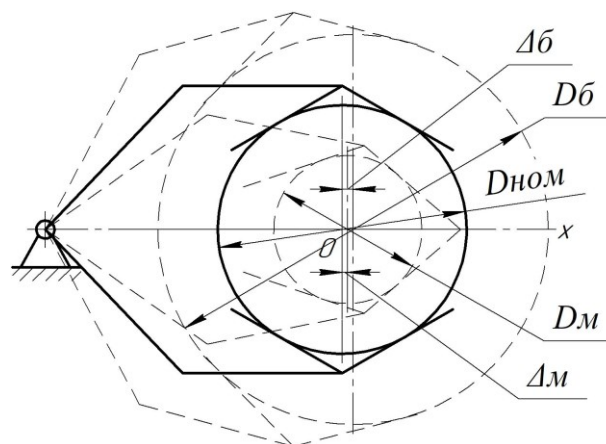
Положення деталей різних розмірів в захватному пристрої
